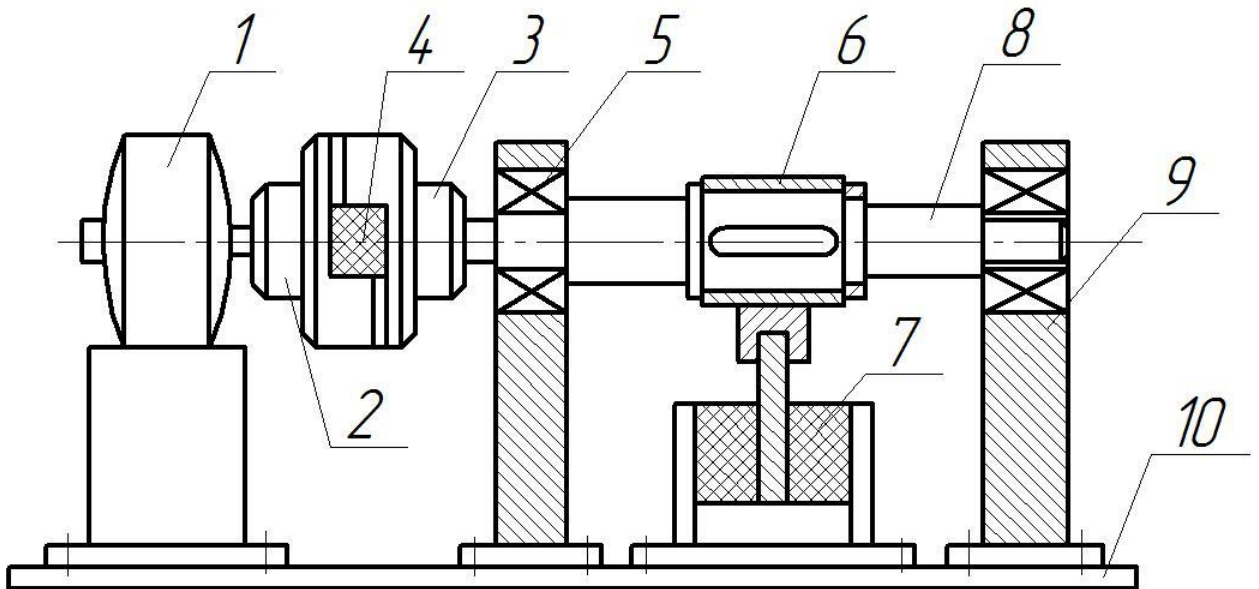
Кинематическая схема испытательного стенда: 1 – электродвигатель; 2,3 – полумуфты; 4 – упругий элемент; 5 – подшипник; 6 – кулачок; 7 – виброизолятор; 8 – вал; 9 – корпус подшипника; 10 – основание
